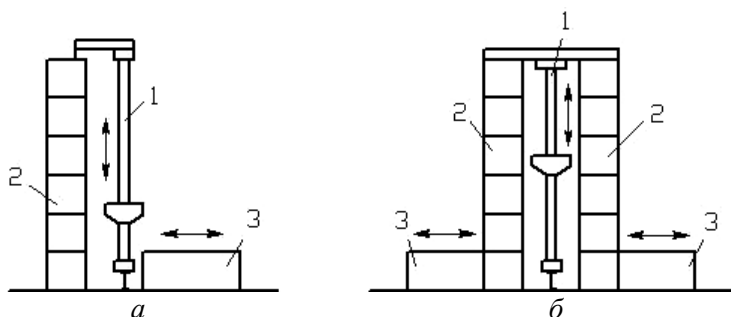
Типовые схемы складов ГАП с автоматическим стеллажным краном-штабелером 1, одним (а) и двумя (б) стеллажами 2 и перегрузочными устройствами 3
